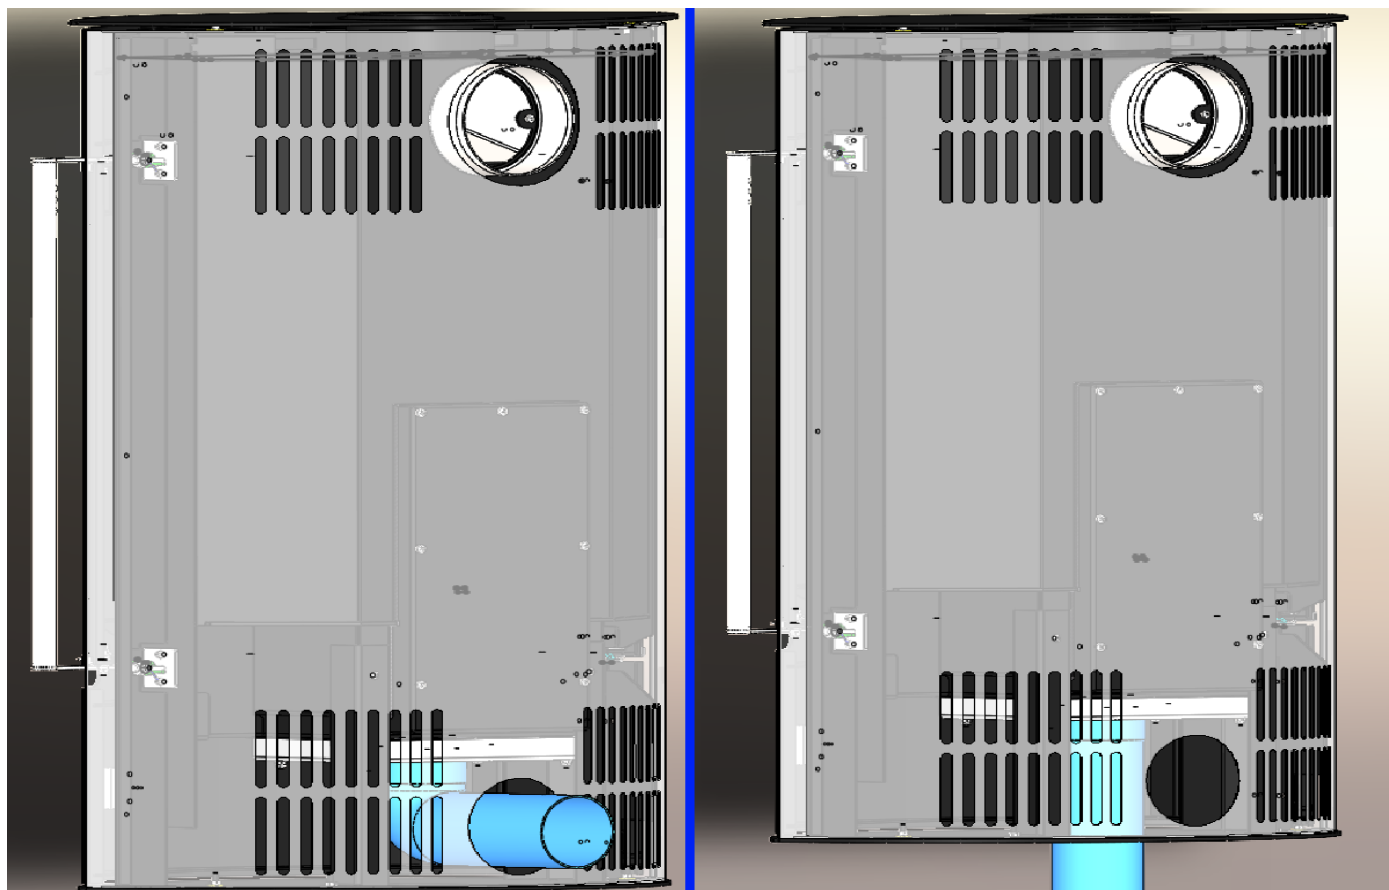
Výměna spoje kouřovodu a krytu kouřovodu
